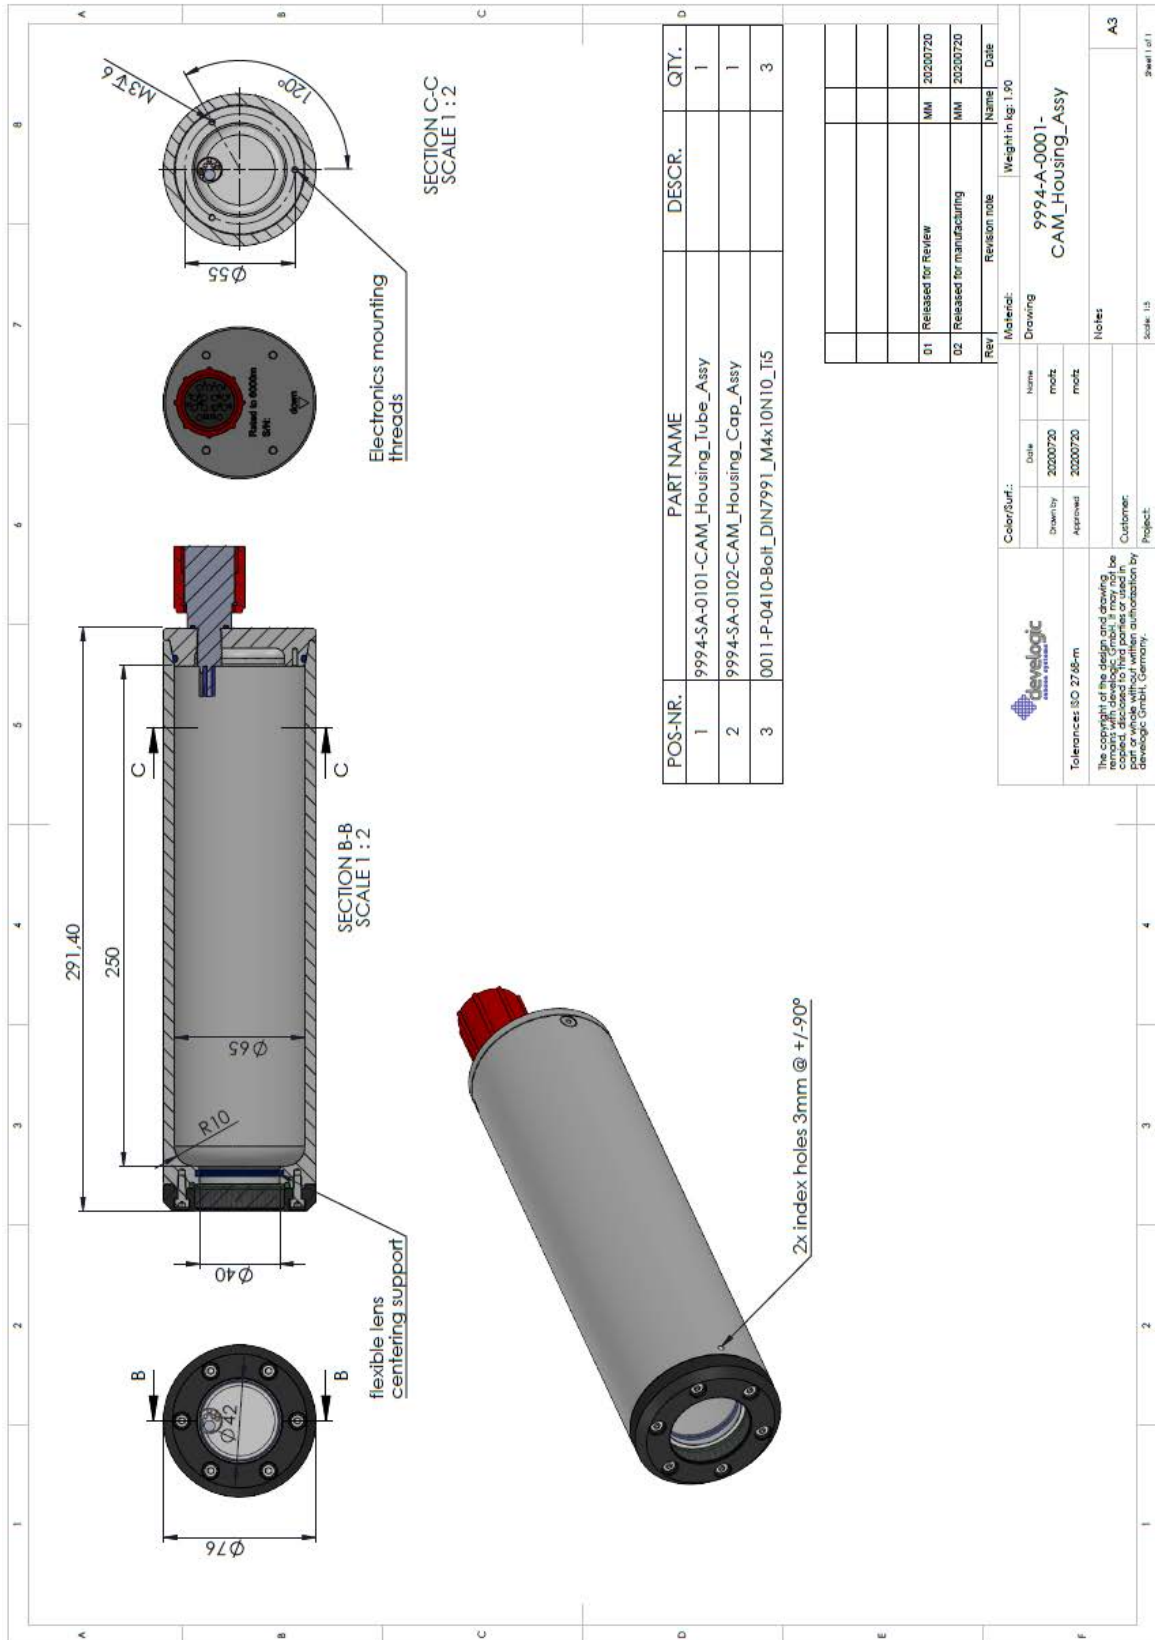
Desenho técnico de construção do encapsulamento da câmera.
